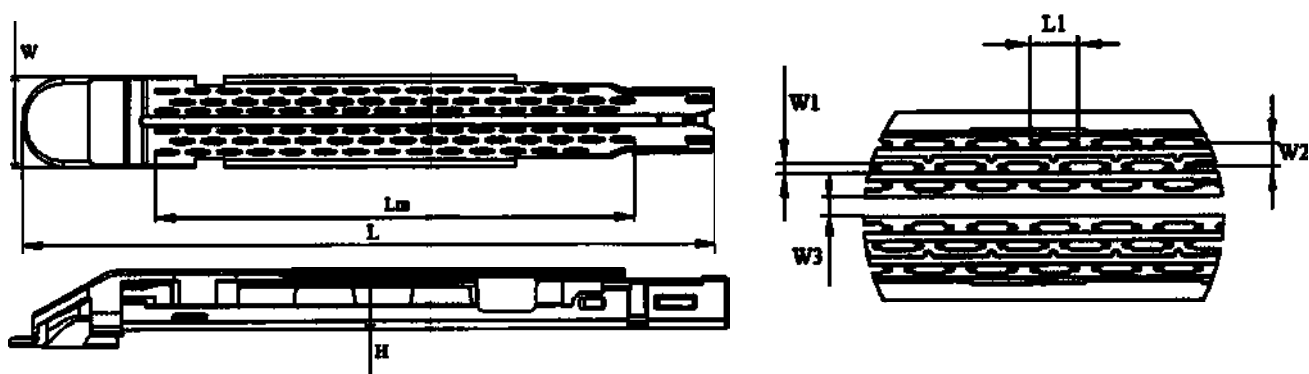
Чертеж блока загрузочного с кодировками вариантов исполнения CN-CCN и CN-CCD
